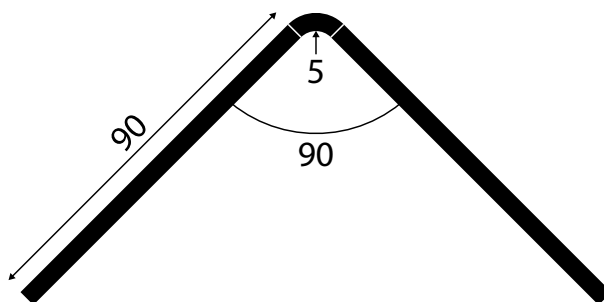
Géométrie de l'éprouvette en L (dimensions en millimètres, angle en degrés)
